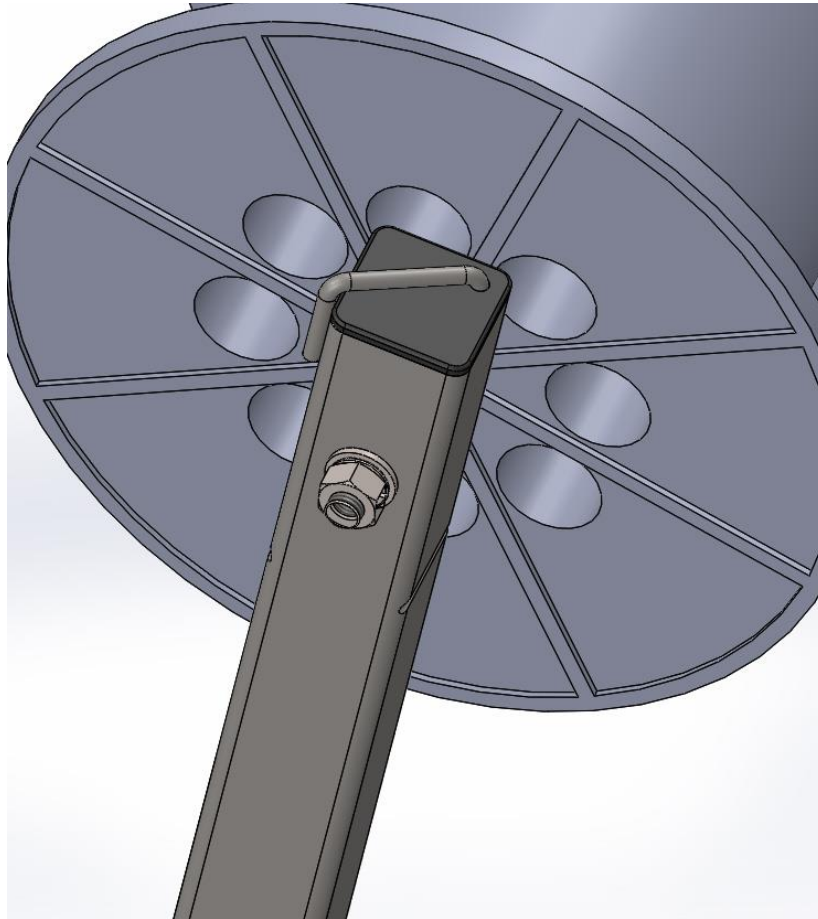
Parte superior del ensamblaje de la bobina durante el uso de la misma.
